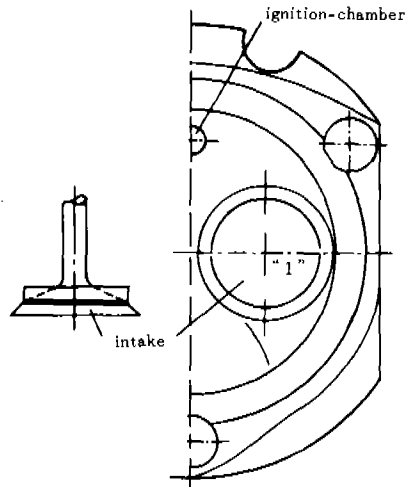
선택된 shroud position을 갖는 valve 안배의 도시적 표현
